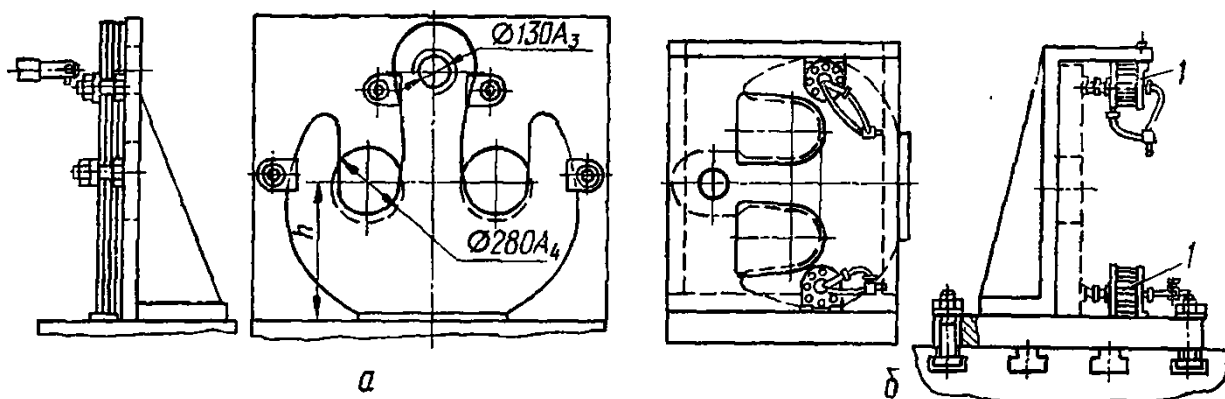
Схемы установки пластинчатого крюка для обработки на горизонтально-расточном станке:
